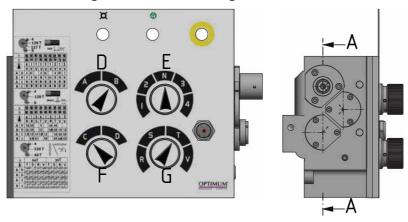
Vorschubgetriebe 1-6 - Feed gear 1-6
